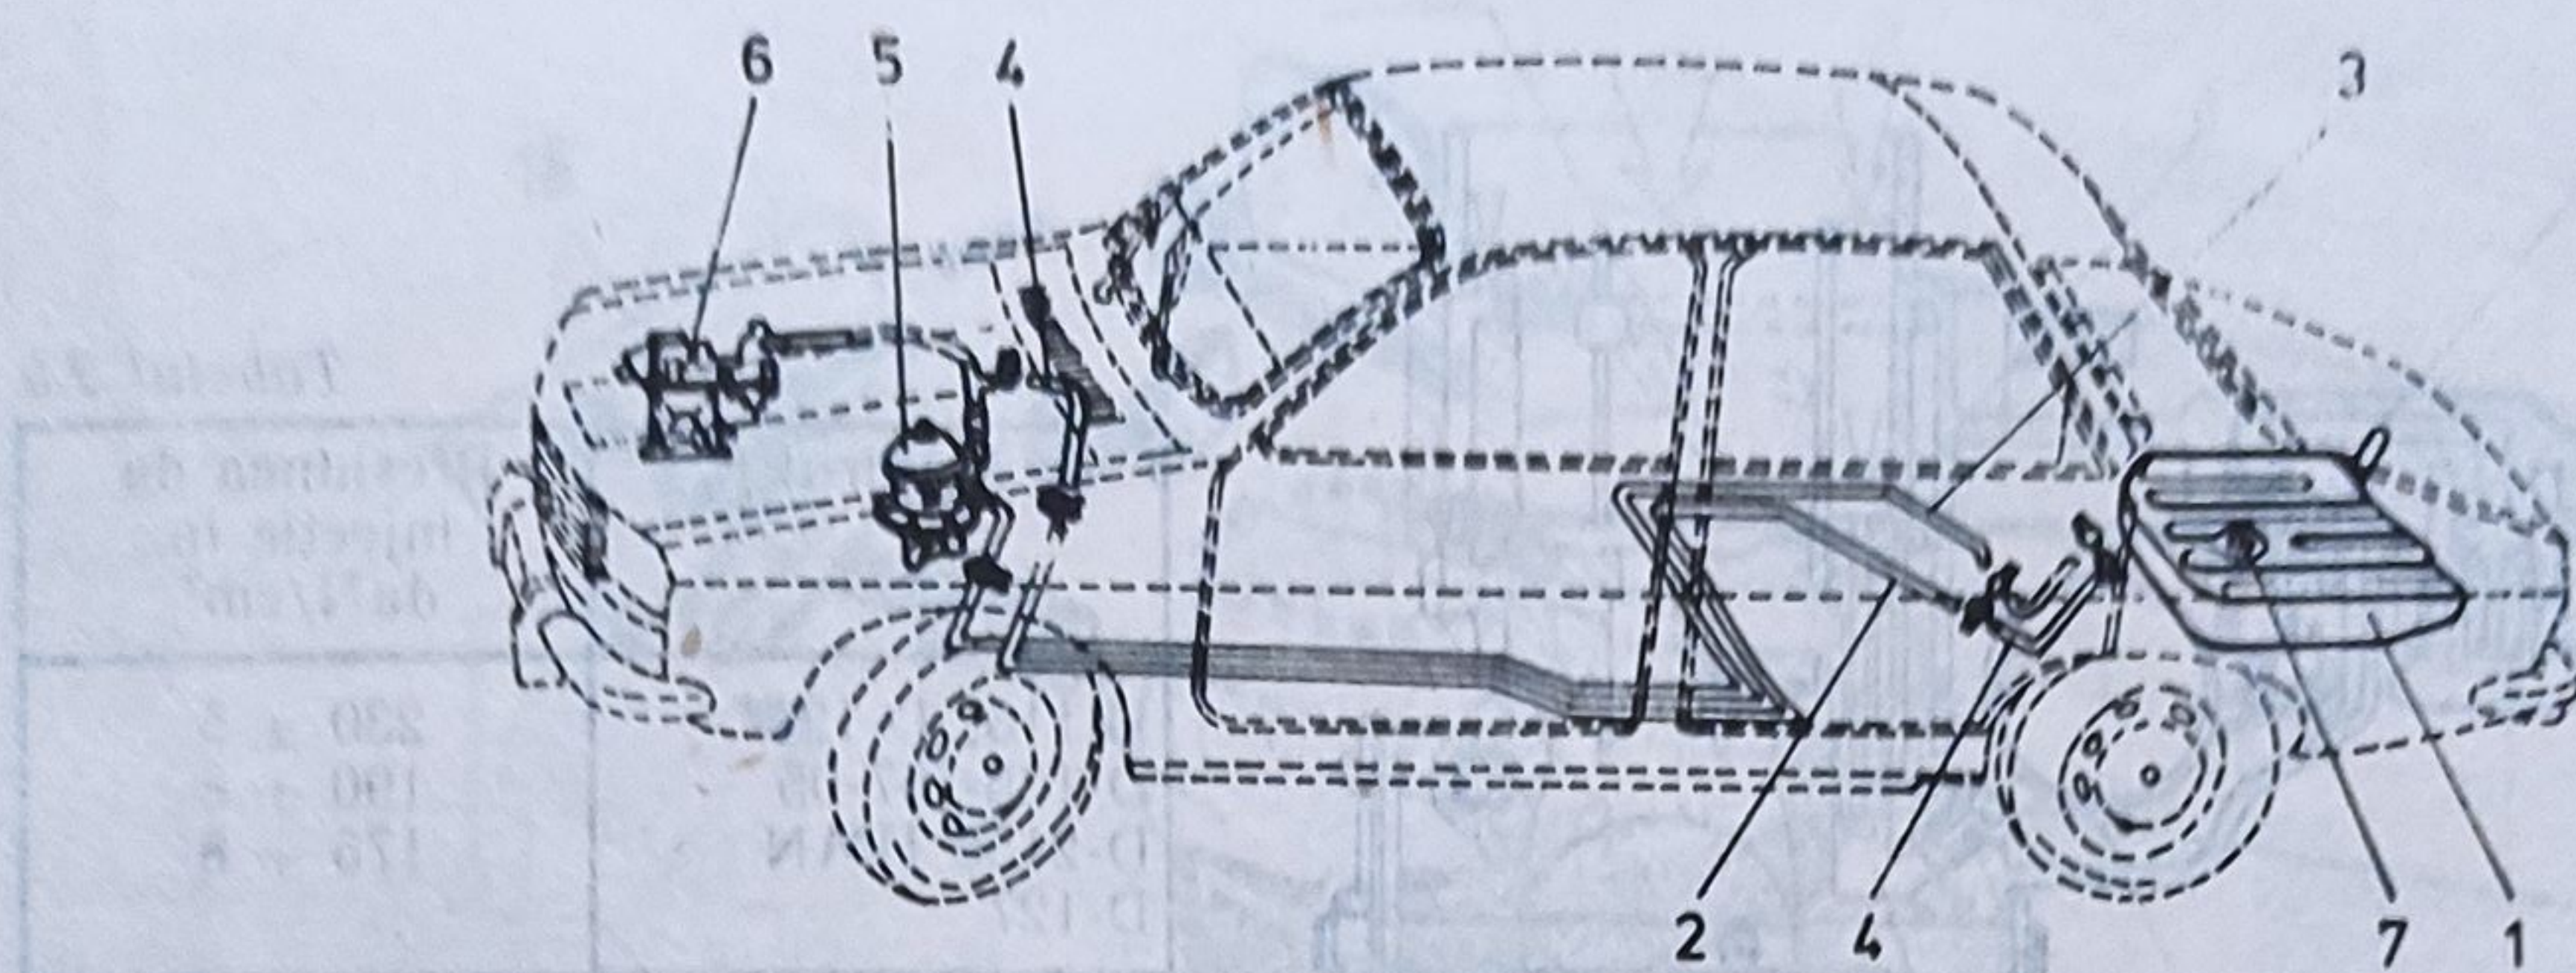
Sistemul de alimentare cu combustibil a motorului de pe autoturismul Dacia 1300, 1310: 1 — rezervor de combustibil; 2 — conductă de retur; 3 — conductă de alimentare; 4 — racorduri elastice din cauciuc; 5 — pompă de benzină; 6 — carburator; 7 — traductor de nivel combustibil.
